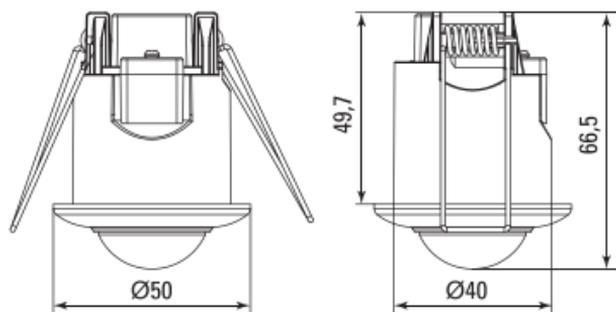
Габаритные и установочные размеры датчика MS-200
